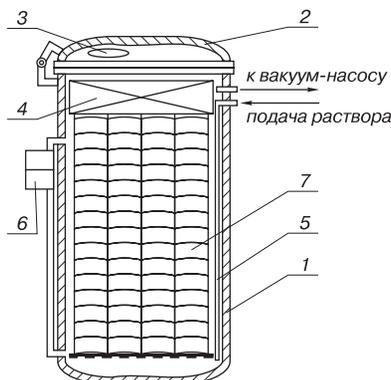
Пропиточный цилиндр: 1 – стальной цилиндр; 2 – герметичная крышка; 3 – иллюминатор; 4 – фиксатор от всплытия заготовок; 5 – система подачи раствора; 6 – насос для перемешивания раствора; 7 – деревянные заготовки
